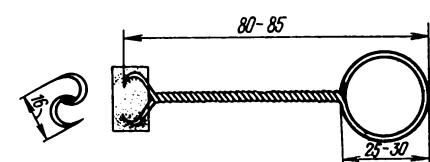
Крейцер для разрядки патронов конструкции С. Никитина и А. Степанова
